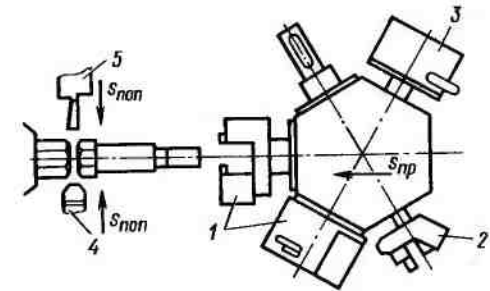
Схема наладки револьверного станка для обработки болта из шестигранного прутка:
